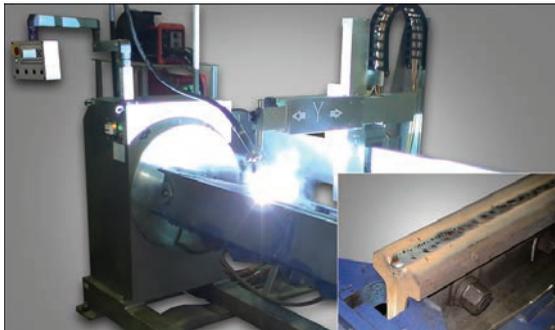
Установка АС364 для автоматической дуговой сварки продольного шва рельсовой части сварной крестовины
